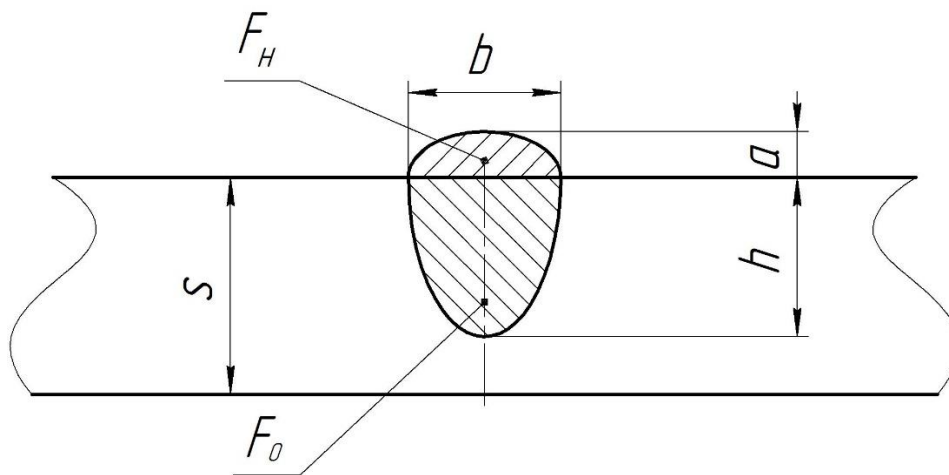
Основні геометричні розміри стикового шва при однобічному зварюванні
